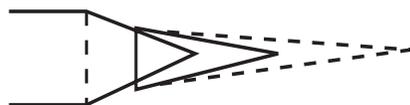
Оптимальный вид пламени горелки для пайки твердым припоем: 1 — факел пламени, насыщенный газом; 2 — факел ярко синего цвета
